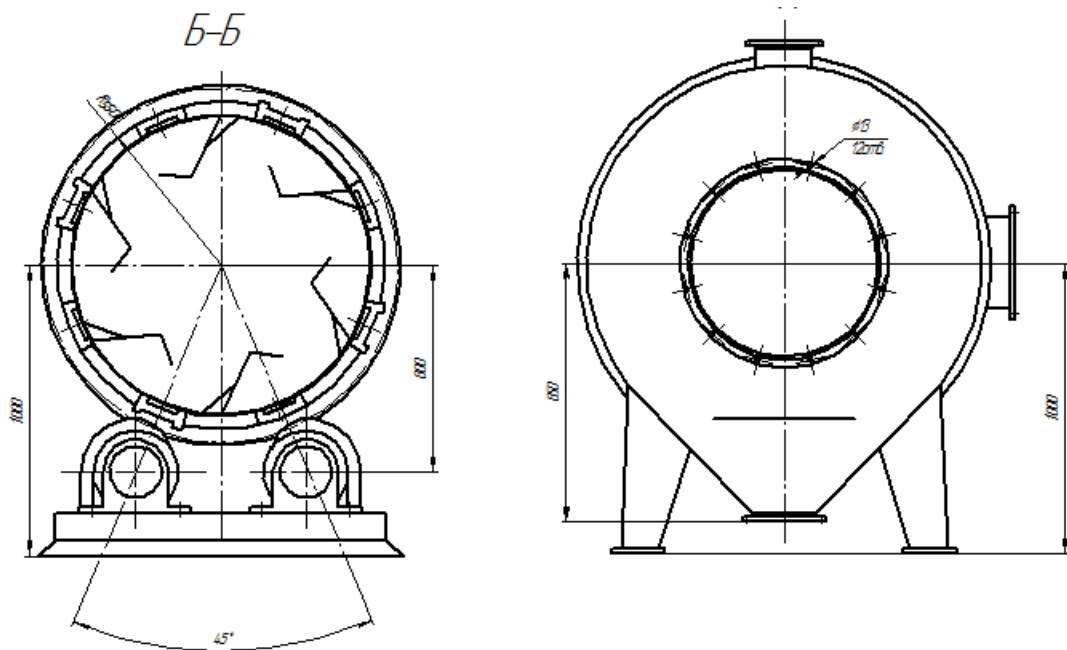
Загальний вигляд барабанної сушарки марки СЗСБ-8А
